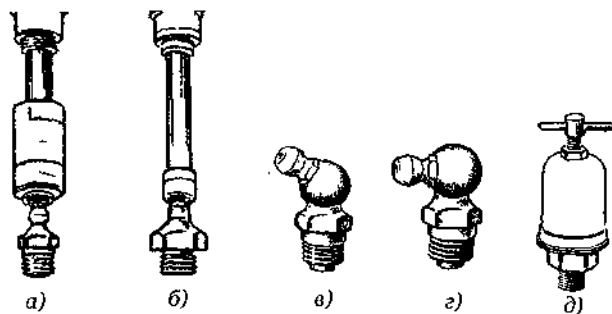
Пресс-масленки различных конструкций: а — с конусной головкой под наконечник нагнетателя с захватывающими цапгами; б — с круглой головкой под наконечник со сферической выемкой; в — с конусной головкой, расположенной к оси штуцера под углом 45°; г — с конусной головкой, расположенной к оси штуцера под углом 90°; д — колпачковая
